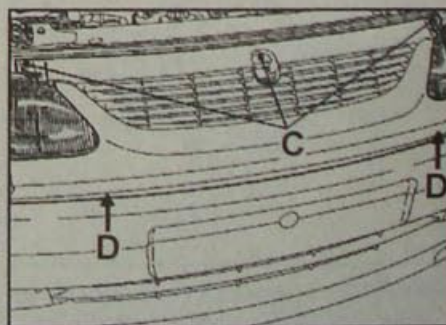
Расположение болтов (C и D) крепления облицовки радиатора
